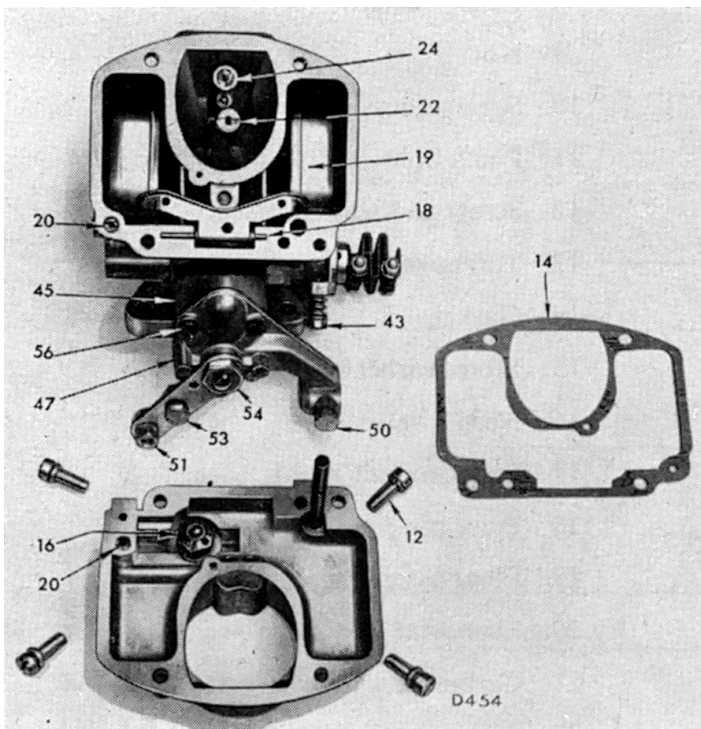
Vue éclatée du couvercle supérieur et de cuve à niveau constant
